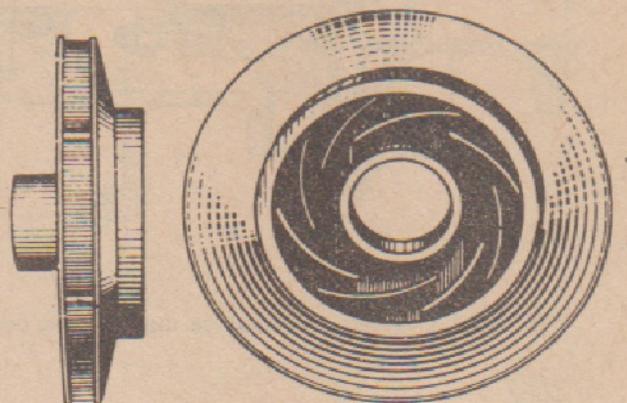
Vistas frontal y lateral del rodete de una turbomáquina
